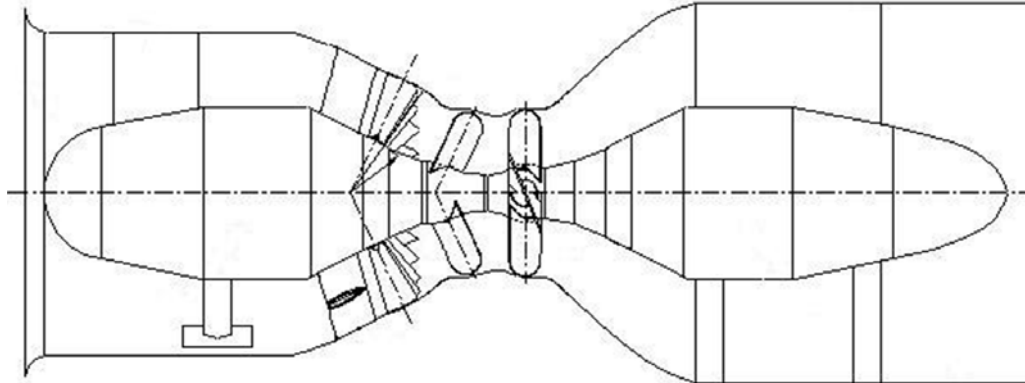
Сдвоенный прямоточный гидроагрегат
